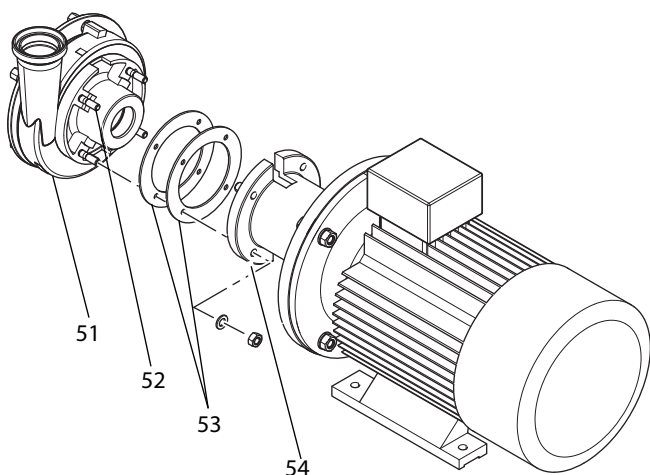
Montaggio del corpo pompa con giunto a flangia
